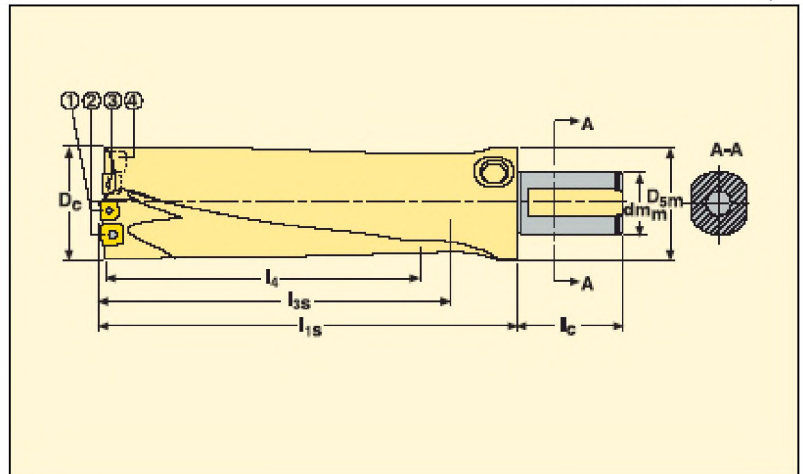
Свердло зі змінними твердосплавними пластинами
